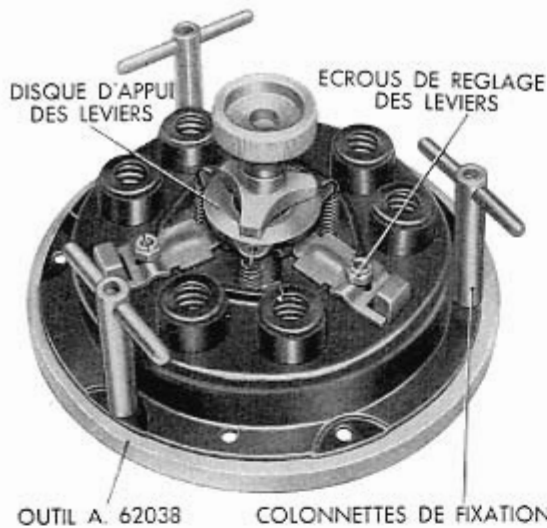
Outil A. 62038 pour démonter, monter et régler l'embrayage.
